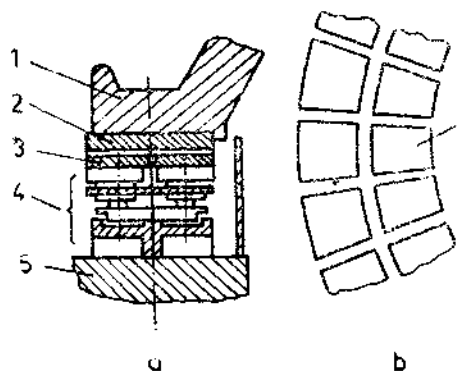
Principiul realizării segmentelor de crapodină: a — secțiune transversală; b — vedere în plan; 1 — piesă portantă; 2 — inel de sprijin; 3 — segmente (cuzineți); 4 — elemente elastice; 5 — steaua portantă.
